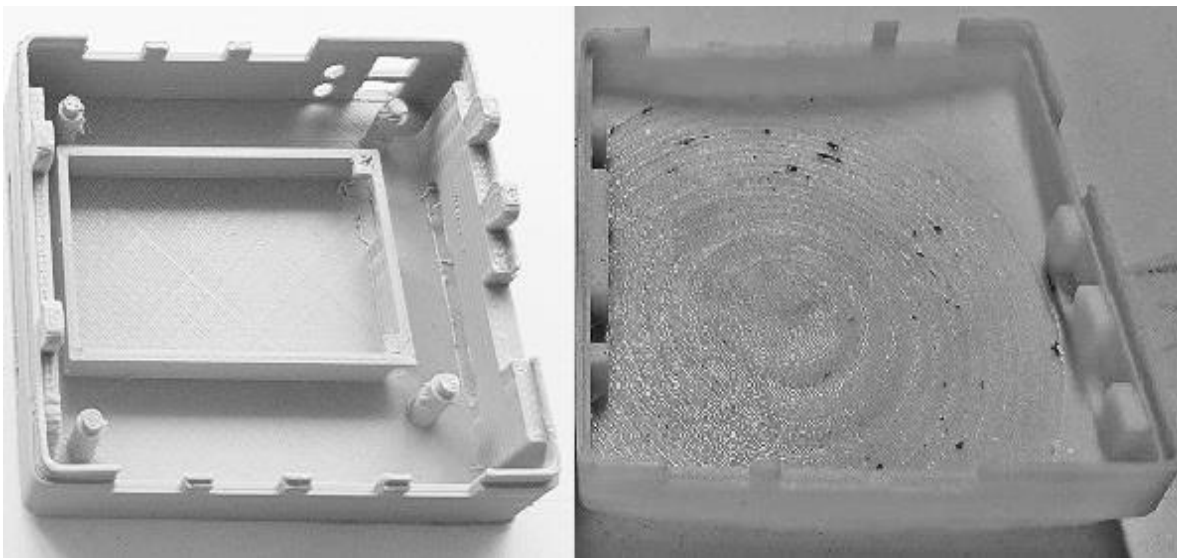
a Carcasa para diseño de tarjeta PCB.
